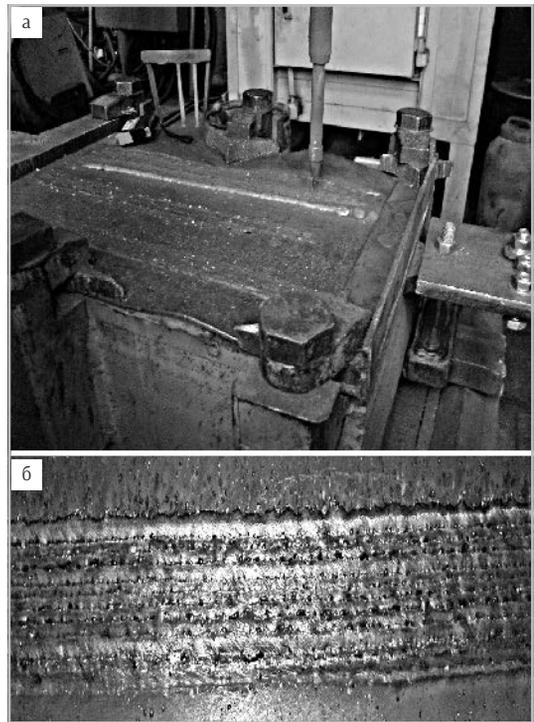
Процесс наплавки стальной пластины толщиной 3 мм самозащитной порошковой проволокой ПП-АН192 (а); фрагмент наплавленного слоя (б)
